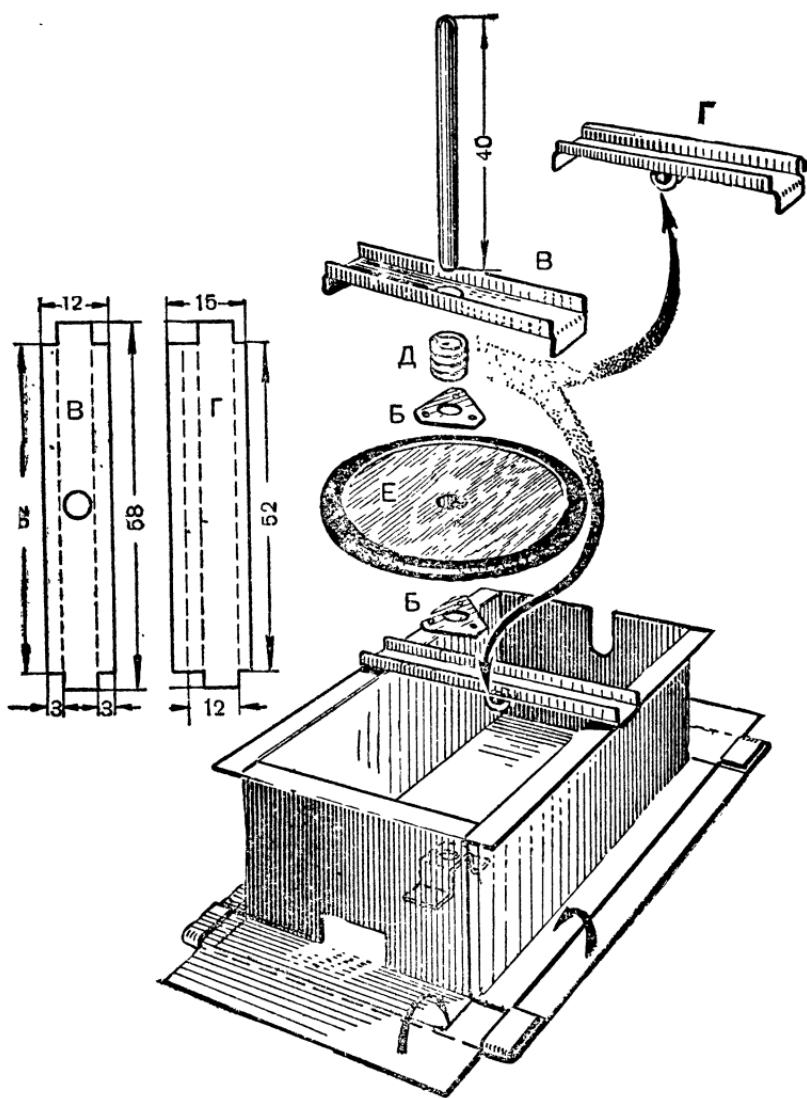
Накладки и порядок сборки редуктора № 5 (рис. 117):
